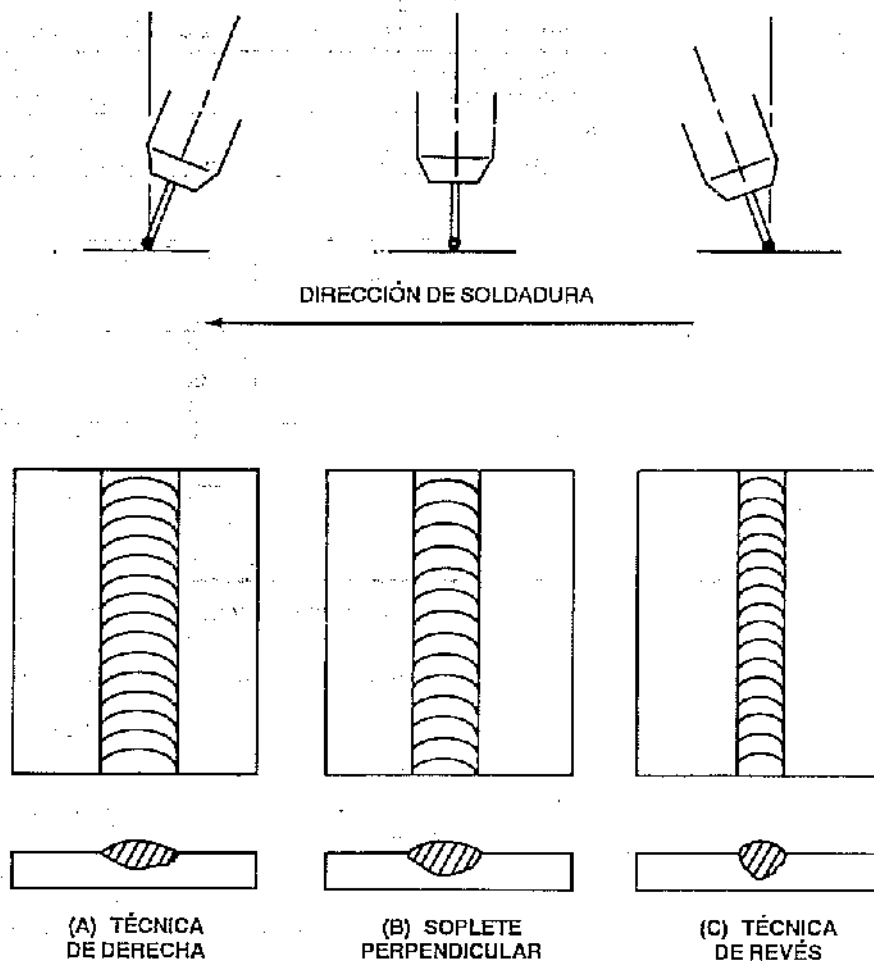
Efecto de la posición del electrodo y de la técnica de soldadura
